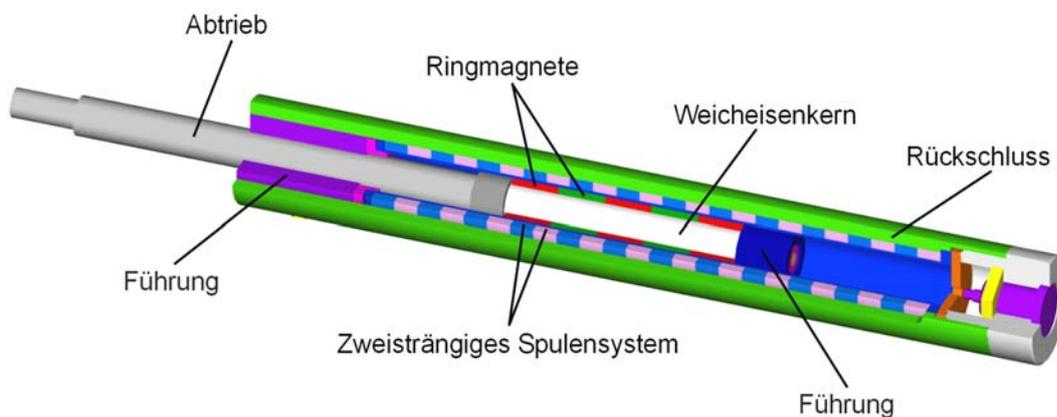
Mehrsträngiger Motor mit integrierter Wegmessung
